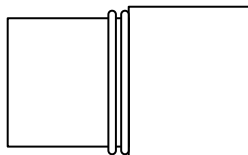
Dvojitá svarová housenka. Viditelná a jednolitá
